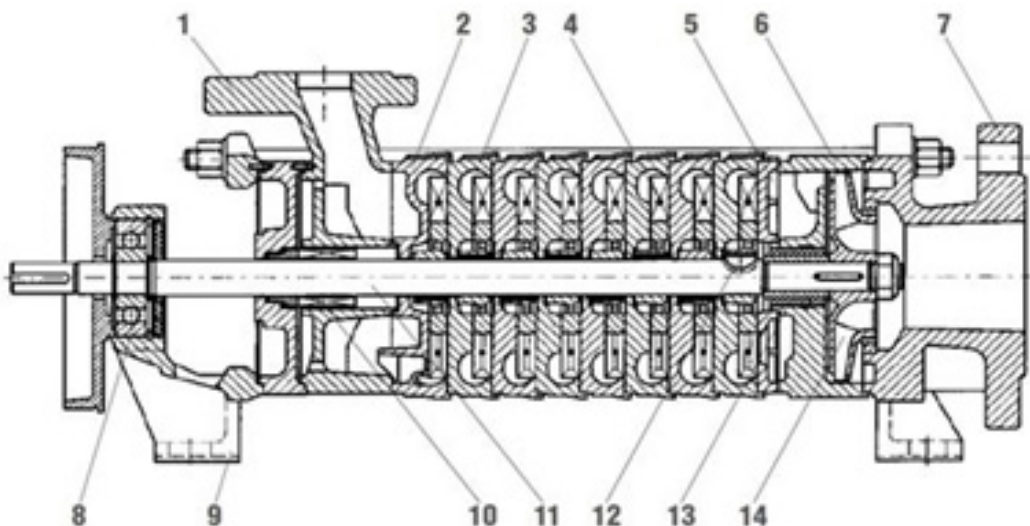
Схема центробежного насоса: 1 – нагнетательный корпус; 2 – нагнетательный блок; 3 – нагнетательно-всасывающий блок; 4 – ротор; 5 – всасывающий блок; 6 – рулевой механизм; 7 – корпус всасывающий; 8 – шарикоподшипник; 9 – корпус подшипника; 10 – уплотнение вала; 11 – вал; 12 – сегментная шпонка; 13 – подшипник; 14 – центробежное рабочее колесо
